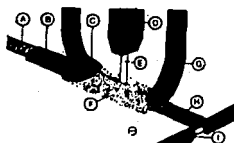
Soldadura por arco sumergido. A) Cordón de soldadura. B) Escoria. C) Eliminador de polvo. D) Soporte del electrodo. E) Metal de aportación. F) Polvo. G) Suministrador de polvo. H) Cordón de raíz. I) Metal base.
